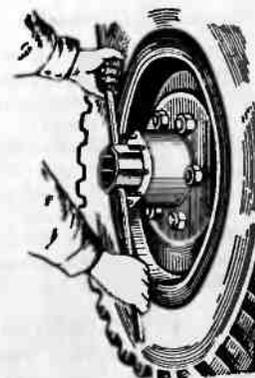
Регулировка подшипников ступицы переднего колеса (затяжка регулировочной гайки)
